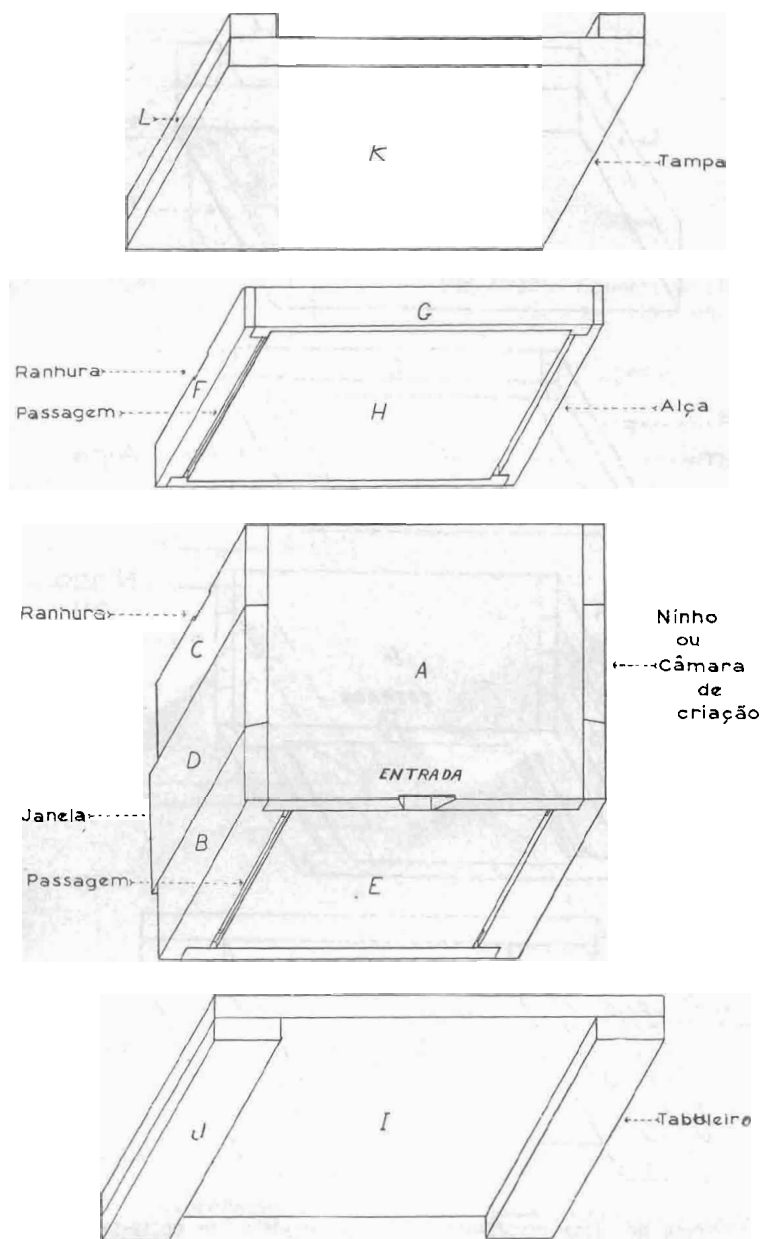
Colmeia de alças em posição normal—tipo 1—vista em pormenor.
